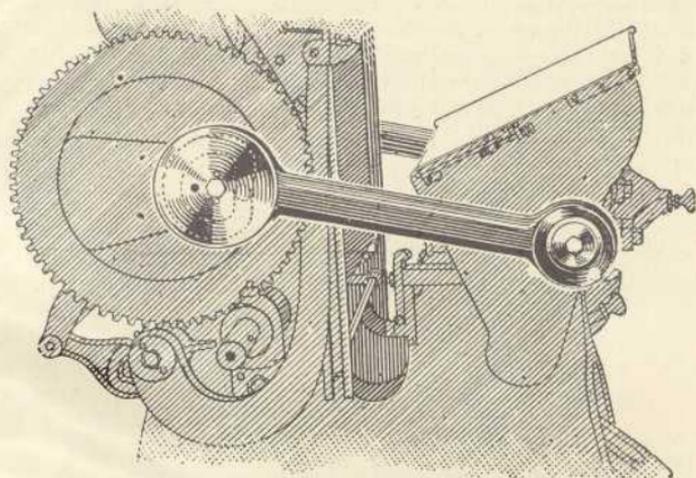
Biela con cojinetes resbalantes, de una máquina de presión plana.
